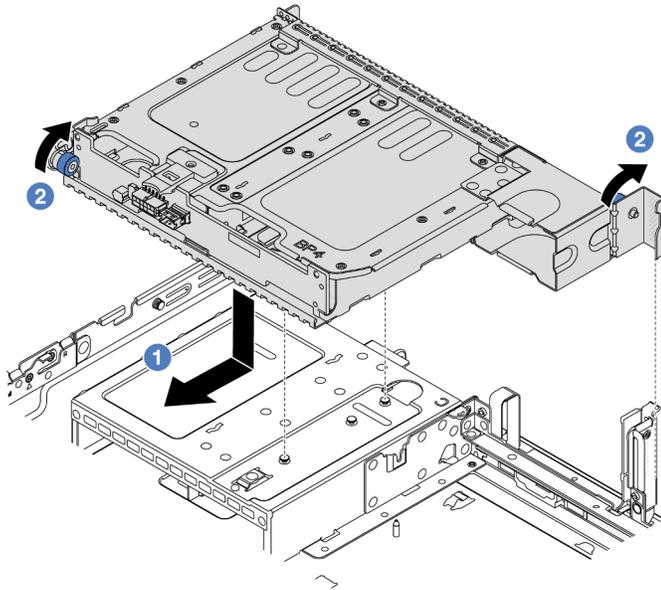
Installation du boîtier d'unités de disque dur arrière 2 x 3,5 pouces
